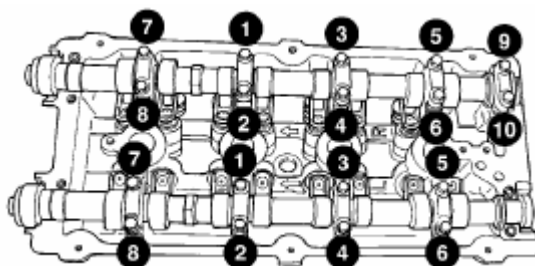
Последовательность затяжки крышек подшипников распредвала.
